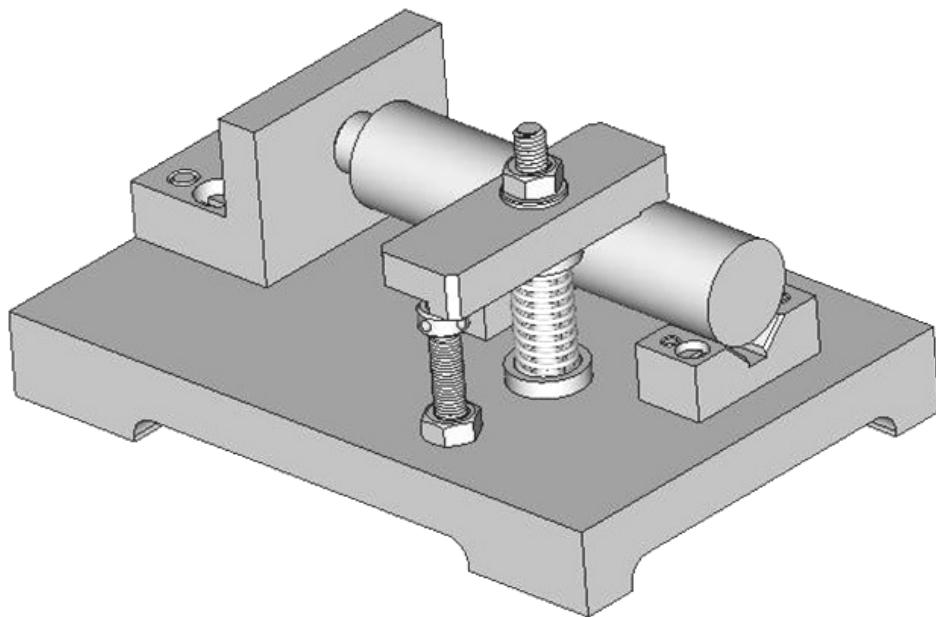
Прихват прямой в приспособлении для установки вала на две призмы
